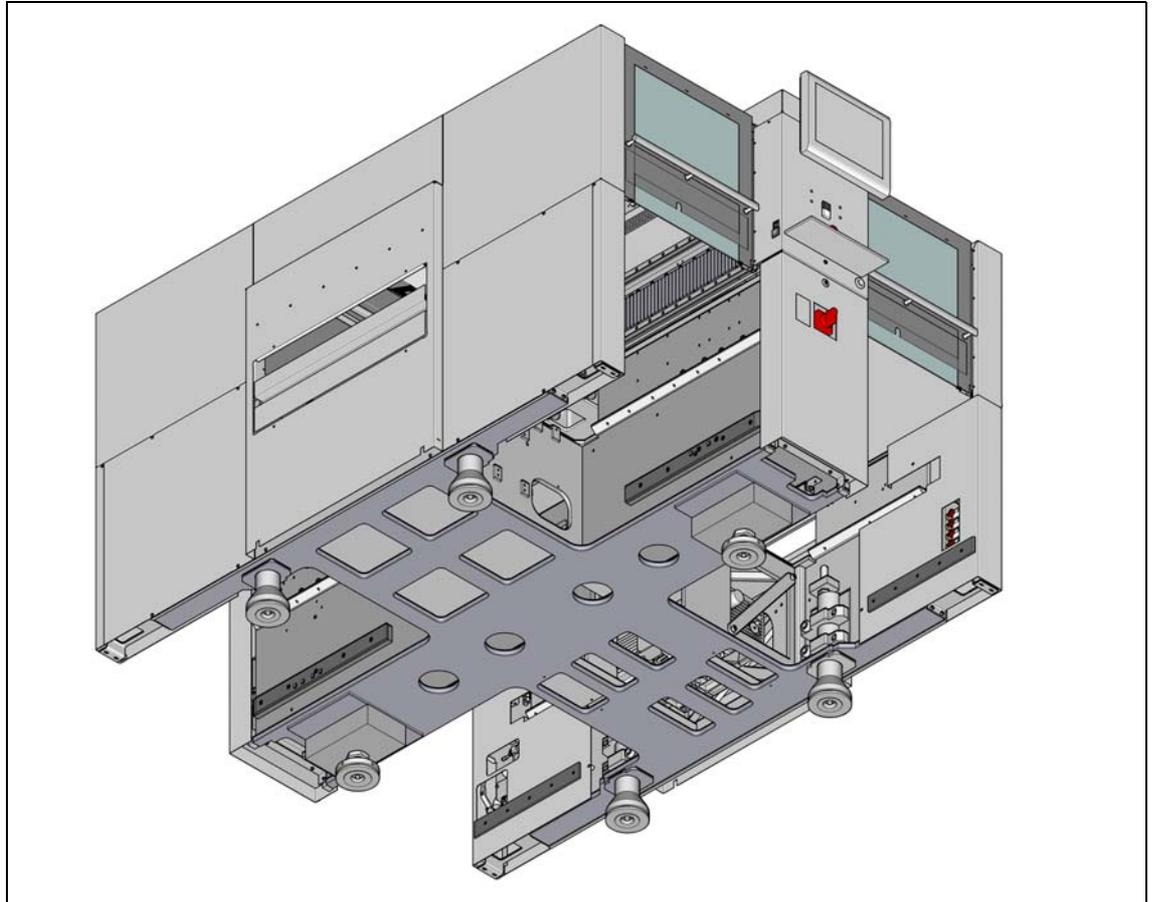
接触表面 - 与 PCB 传送方向平行的货叉 (示例为 SX4)
